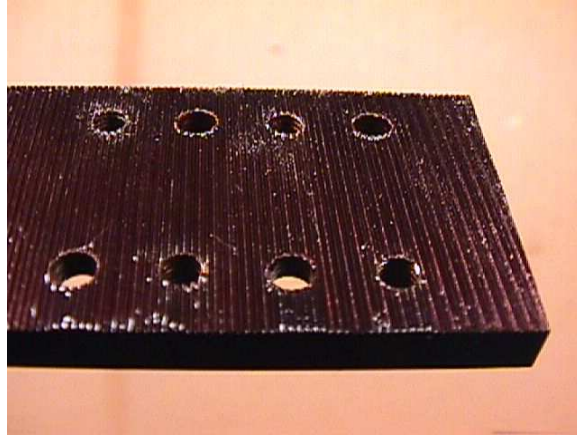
Vista das estrias das amarras do dispositivo para ensaios de tracção.
